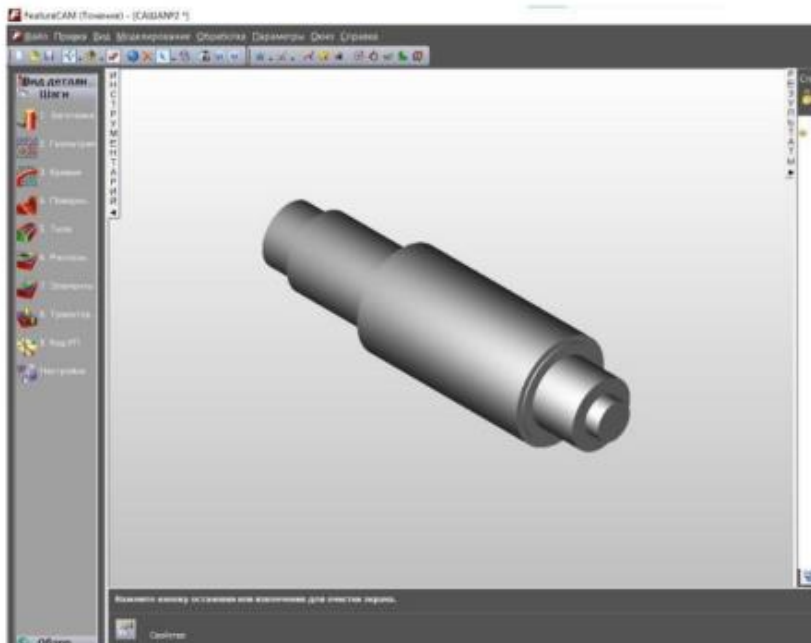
Вал після чорнкової токарної обробки)
